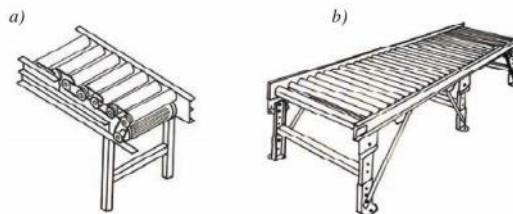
transportadores de rodillos; a) accionado mecánicamente; b) por gravedad [5].
